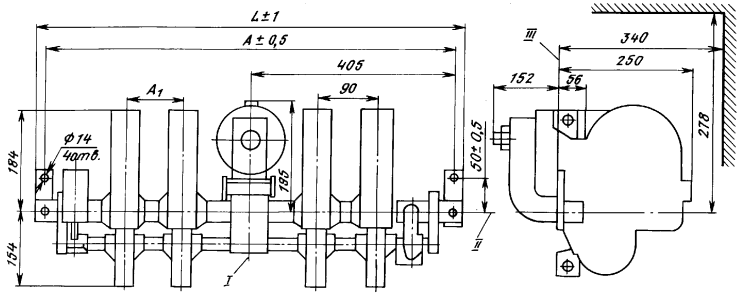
Габаритные и установочные размеры контакторов КТП6044
